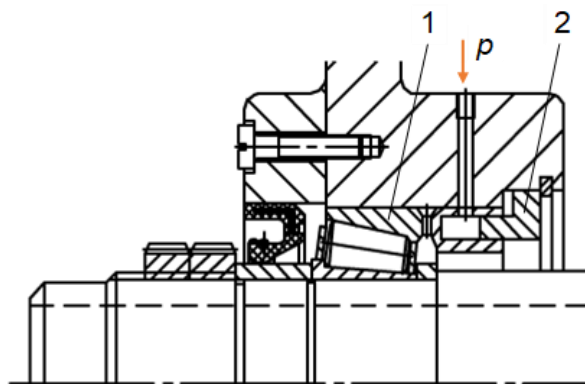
Задня опора ШВ токарного верстата з ЧПК з керованим натягом
